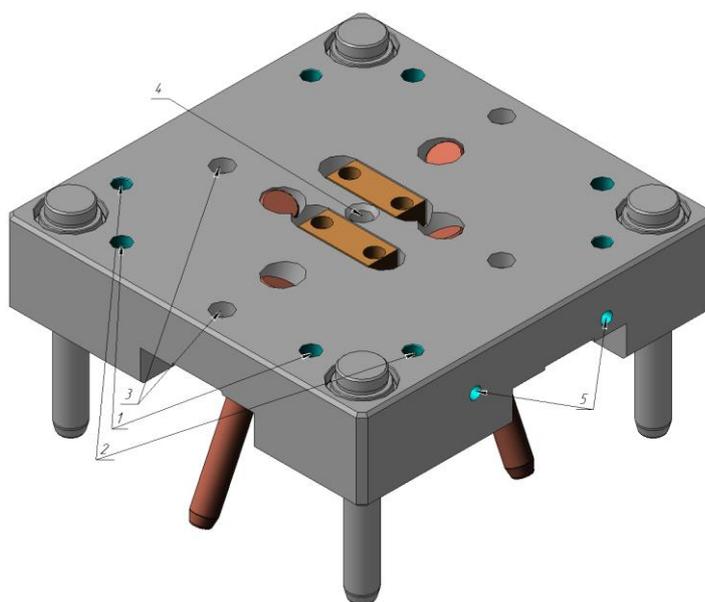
Внешняя сторона плиты MLI после доработки с установленными на ней вставками, клиньями, угловыми и направляющими колонками. 1–отверстия под крепление с плитой KL2; 2–отверстия под крепление с плитой станка; 3–отверстия под крепление клиньев; 4–отверстие центрального литникового канала; 5–каналы охлаждения.
